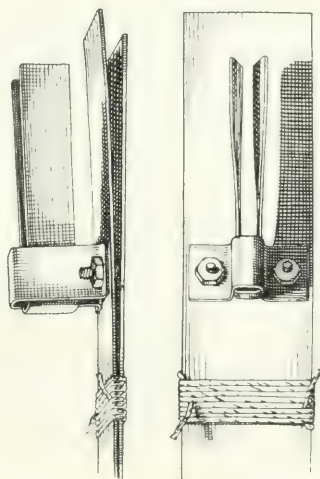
Die „Hand“ der Bumerang-Wurfmaschine.
